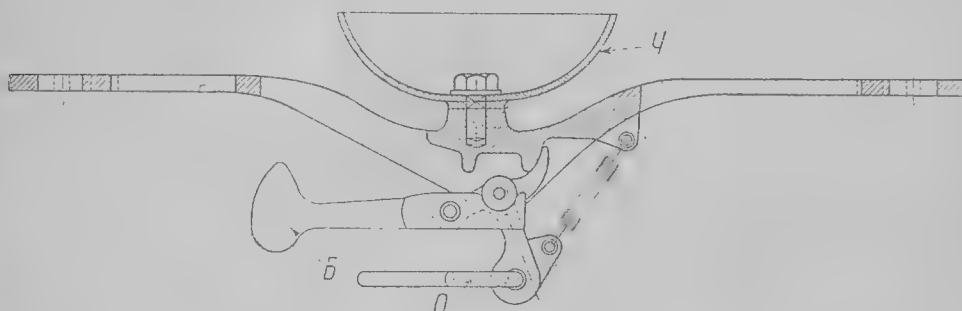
Сигнальный звонок кондуктора: Ч — чашка звонка, Б — боек, О — отверстие для веревки.
